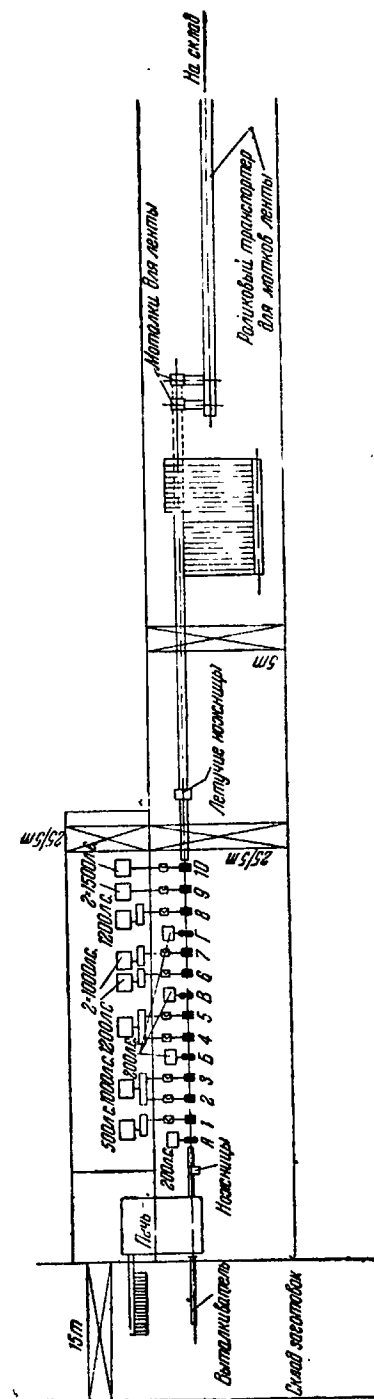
Непрерывный стан для прокатки ленты и заготовки для сварных труб
